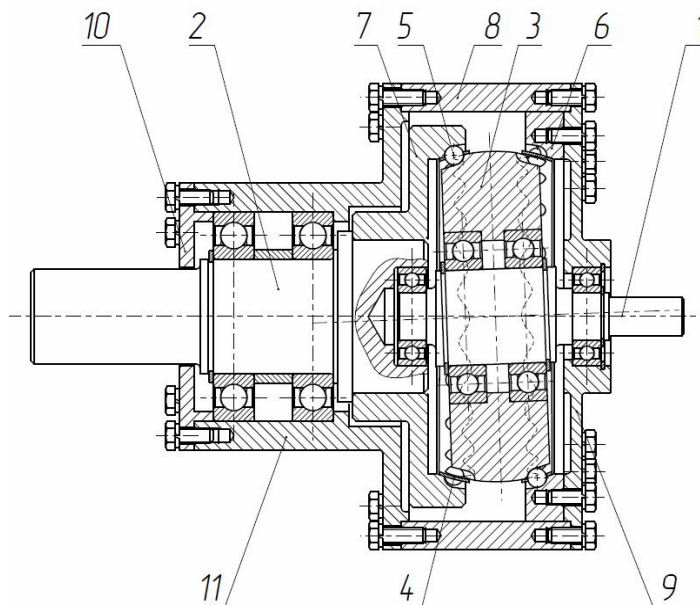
Конструкция двухступенчатой ВППТК: 1 – входной вал, 2 – выходной вал, 3 – прецессионное колесо, 4 – сепаратор, 5 – шарики, 6 – промежуточное колесо, 7 – промежуточное колесо, 8 – корпус, 9 – крышка, 10 – крышка, 11 – стакан
